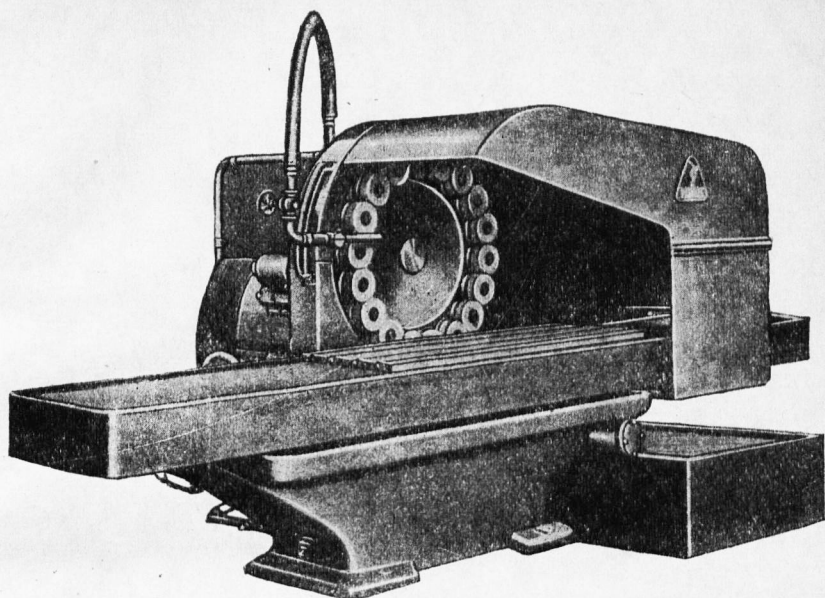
Общий вид плоскошлифовального станка „Дискус“, тип DWN 900/1200
